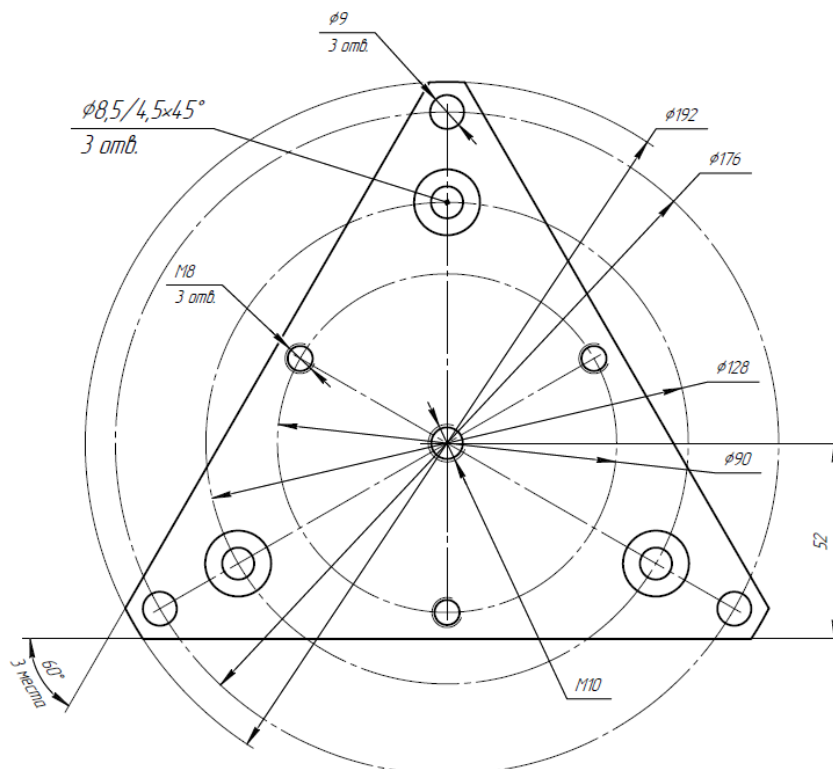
Присоединительные размеры детали «Пластина 1»
